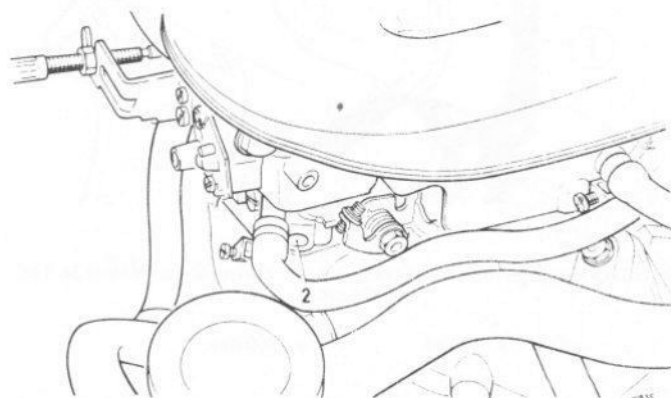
Position de la vis de richesse (2) - carburateur Weber 36 TLC (Sec 8)
